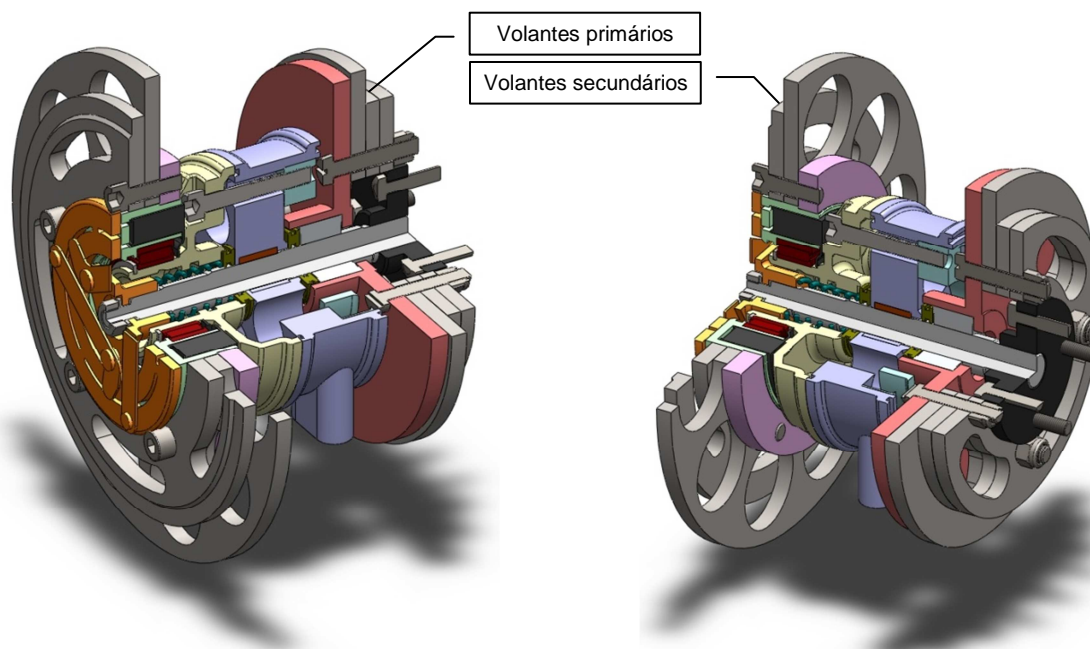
Corte do acoplador mostrando seus detalhes internos e a fixação dos volantes
